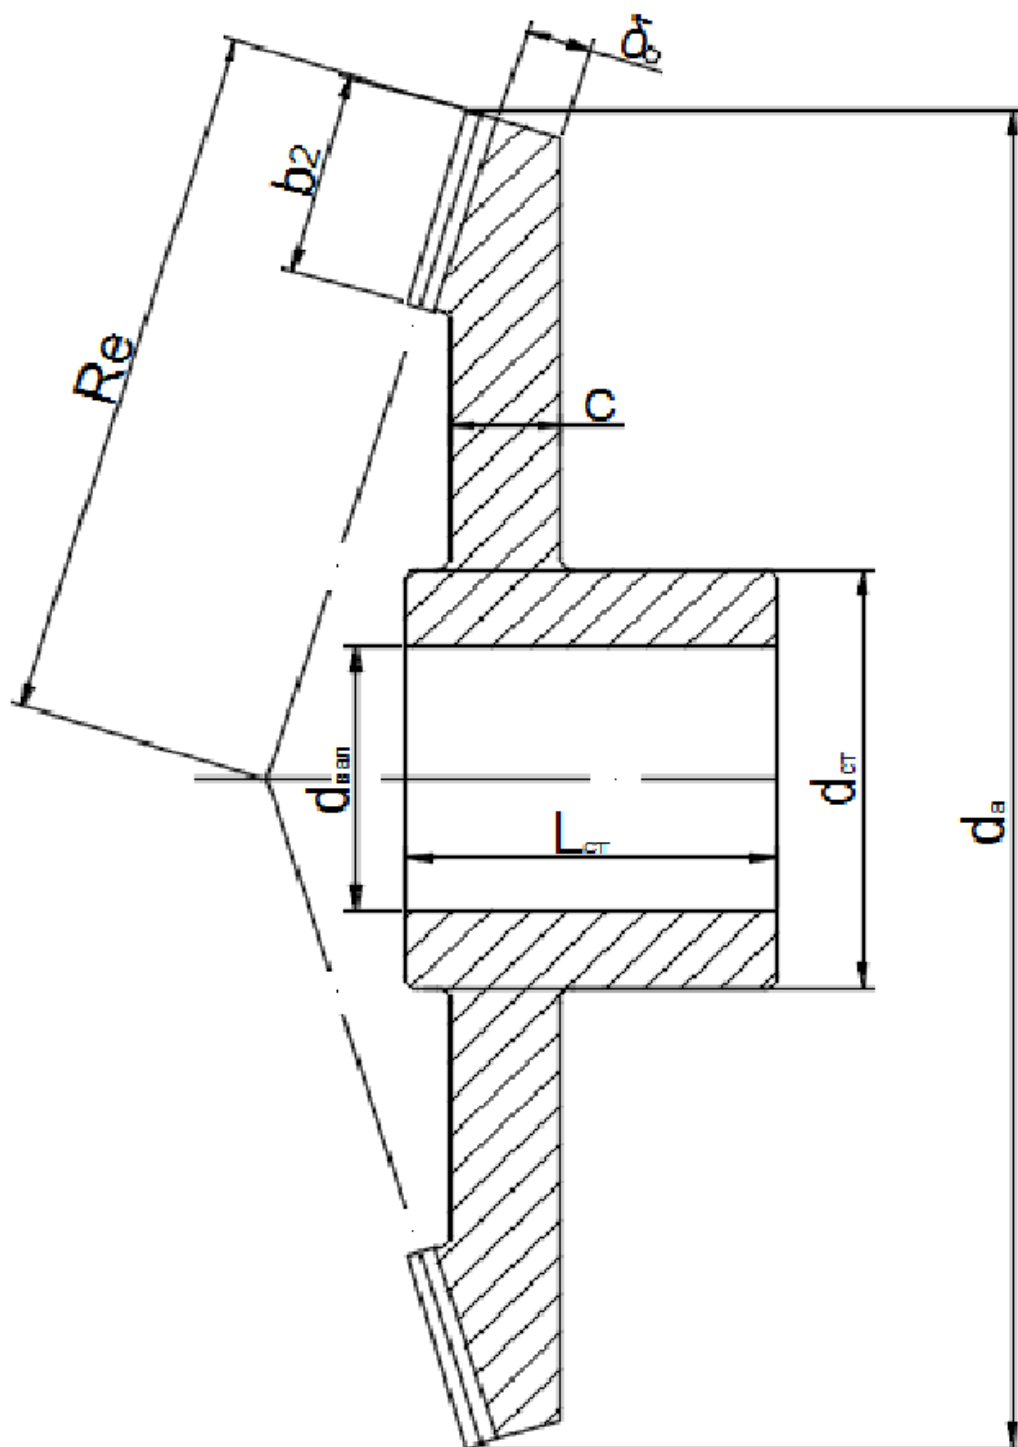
Конструктивные размеры конического зубчатого колеса
